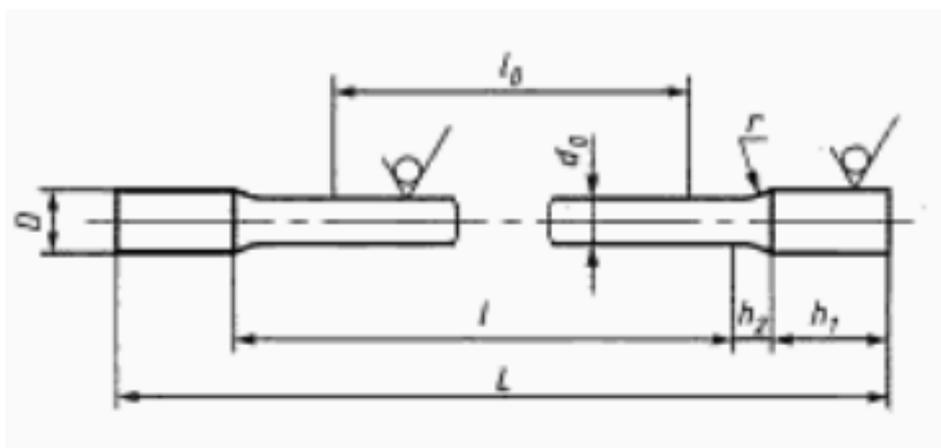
Форма и размеры образца при литье в песчаную форму и кокиль
